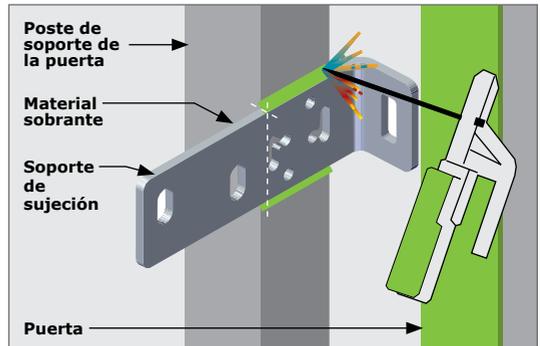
POSTE DE SOPORTE - SOLDADO
